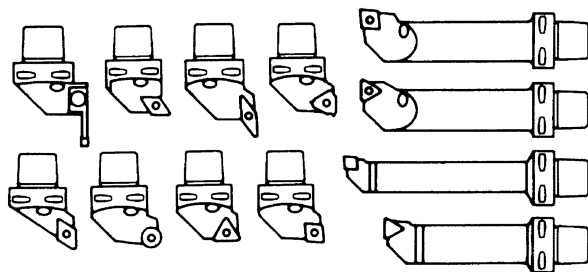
Специальные конструкции проходных, канавочных и расточных резцов для закрепления в резцедержателях токарных станков
